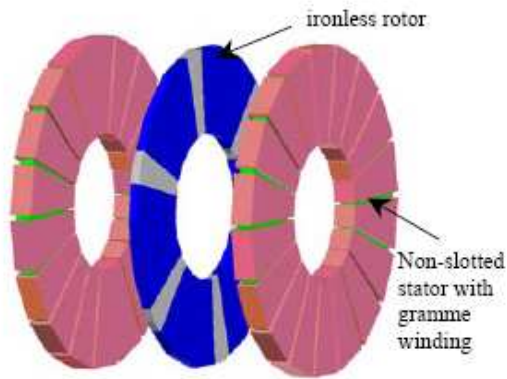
Machine à flux axial 2 stators/ 1 rotor avec bobinage réparti non encoché.
